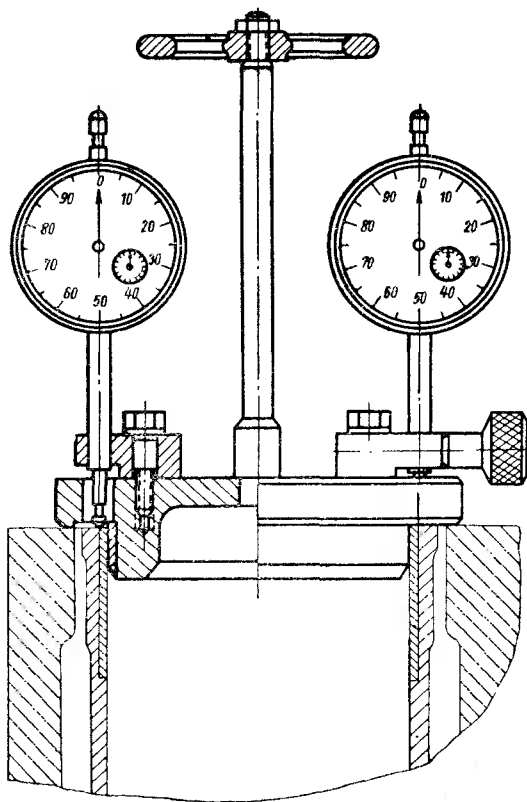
Приспособление для замера расстояния от верхнего торца гильзы до плоскости разъема блока цилиндров с головкой цилиндров
